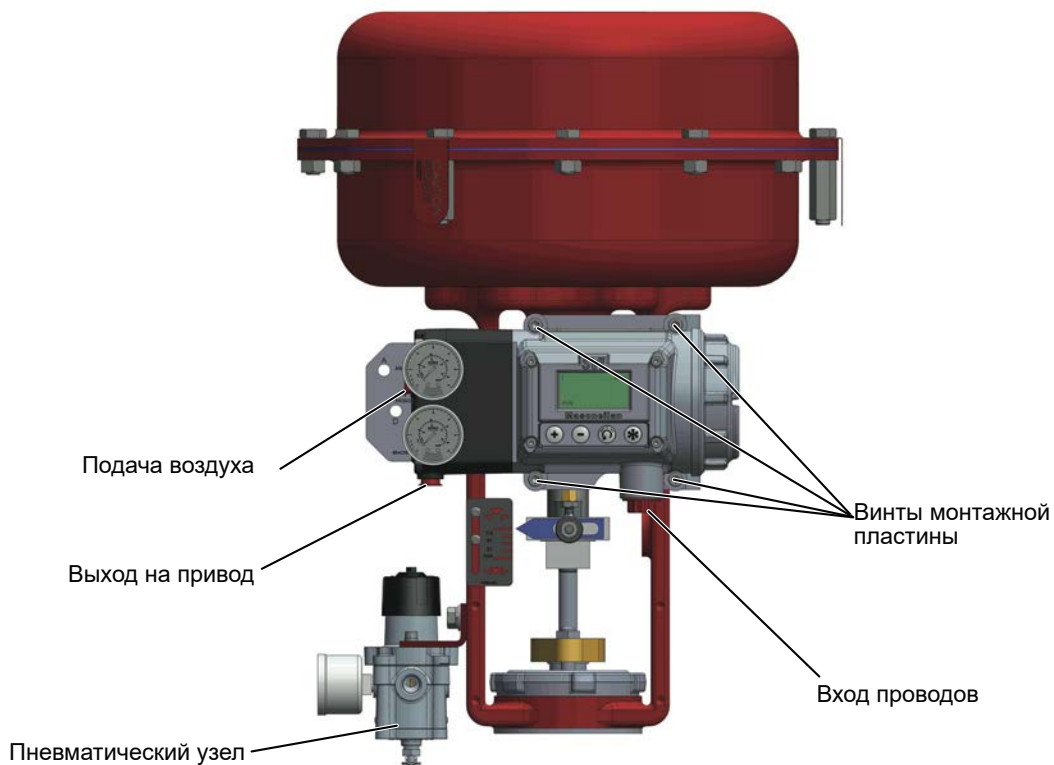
Пример установки на клапан с возвратно-поступательным механизмом
